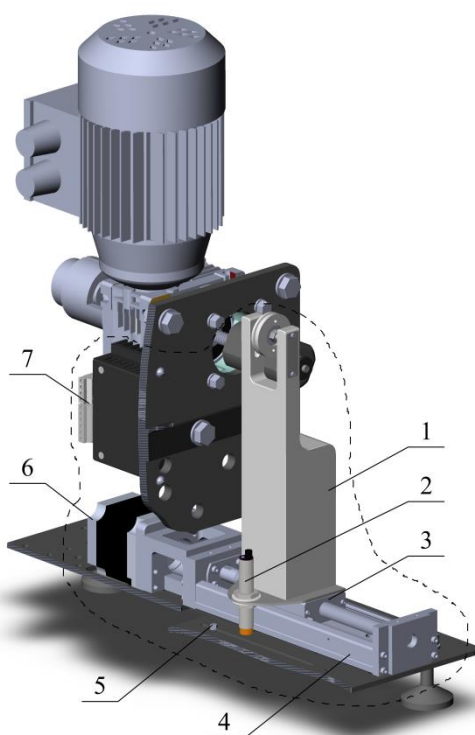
Узел раскладчика установки автоматической намотки катушек чувствительного элемента феррометра: 1 – стойка с роликом; 2 – индуктивный датчик положения; 3 – каретка линейного модуля (4); 5 – нулевая отметка; 6 – шаговый двигатель; 7 – драйвер
